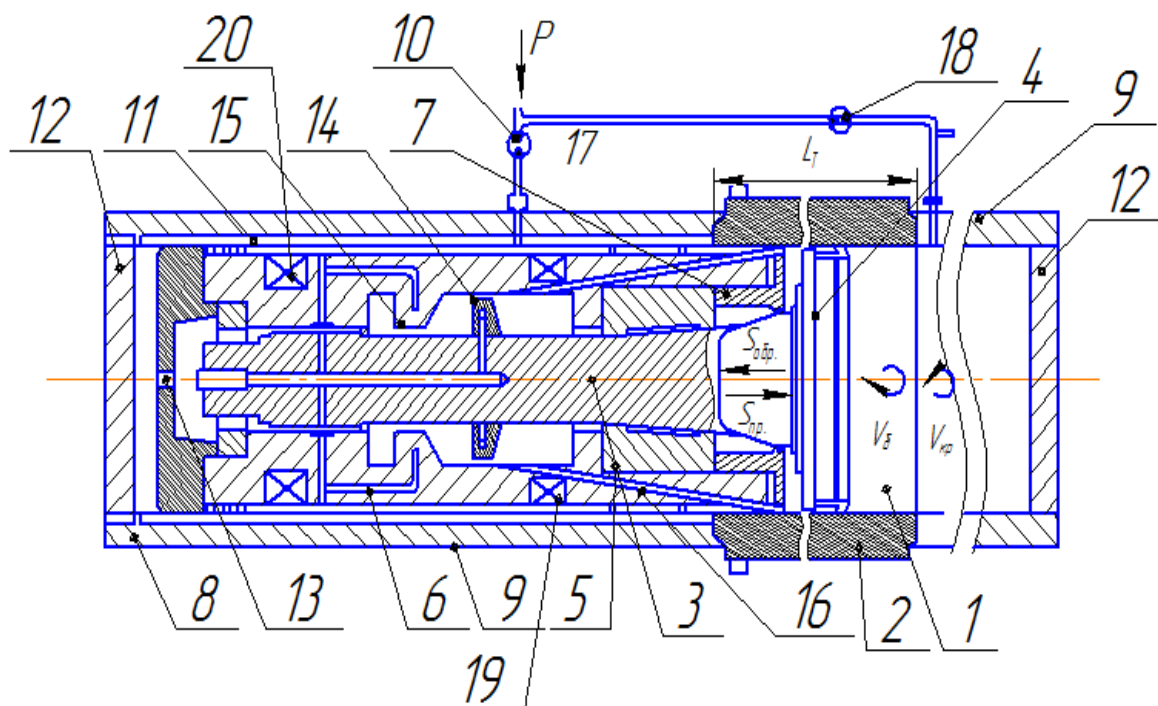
Малогабаритный станок с режуще-деформирующей пинолью для вихрефрезерования ГО труб методом винтовой интерполяции [3]
